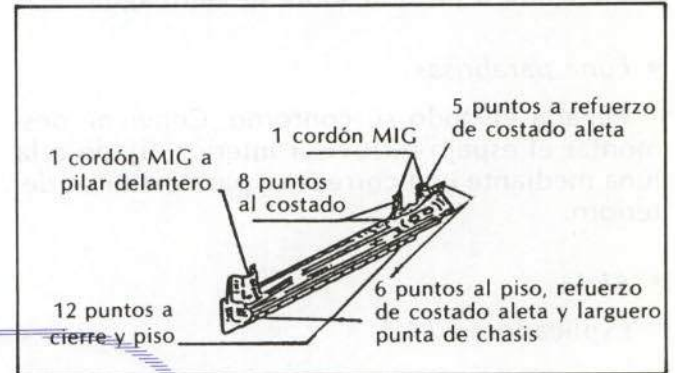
Unión del estribo bajo puertas a la carrocería.
